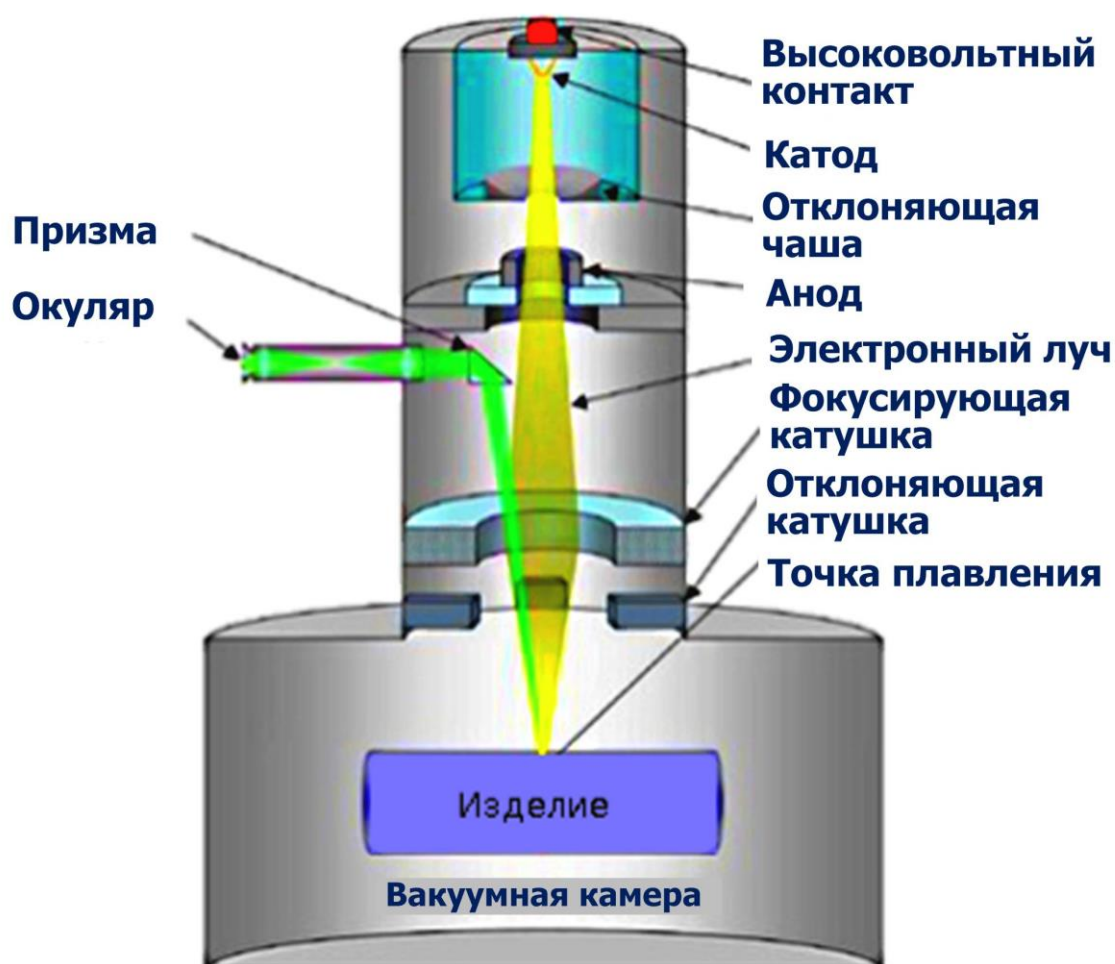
Схема процесса электронно-лучевой сварки
